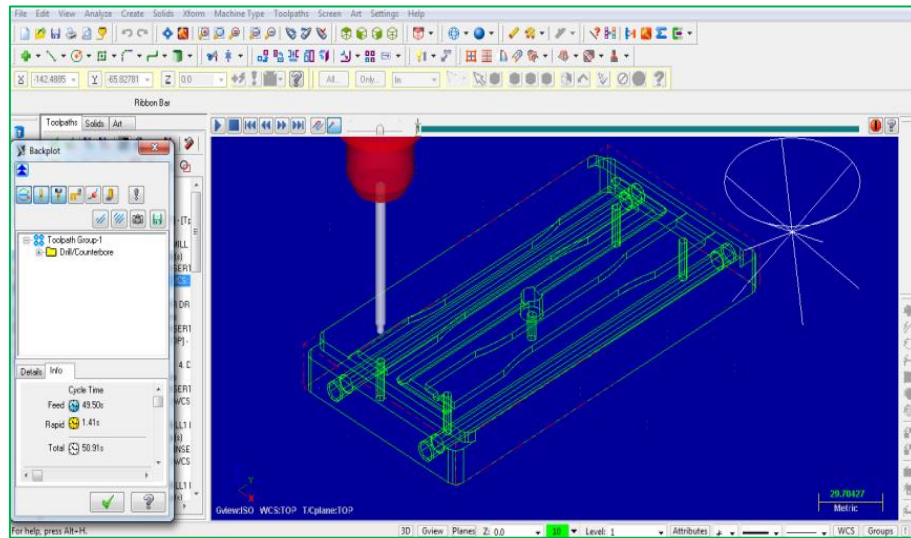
Entorno Master Cam X2 condiciones de trabajo de la herramienta
